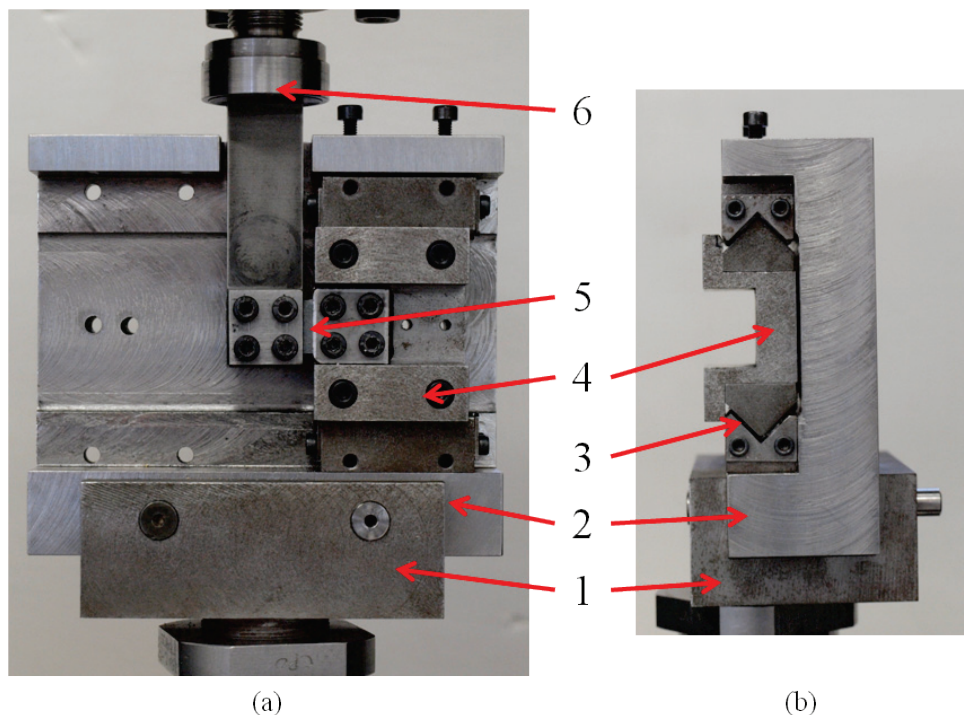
Photographies du montage de cisaillement ; (a) vue de face ; (b) vue de côté ; (1) bâti de fixation à la machine de traction ; (2) bâti principal ; (3) glissière à rouleaux ; (4) partie mobile ; (5) zone cisillée ; (6) mors mobile
